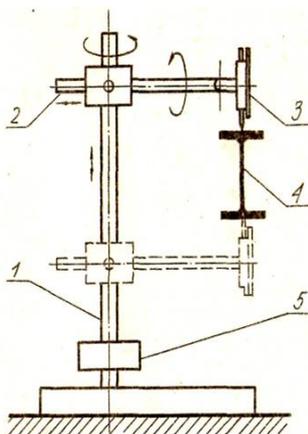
Схема закрепления индикатора: 1 – стойка штатива;
